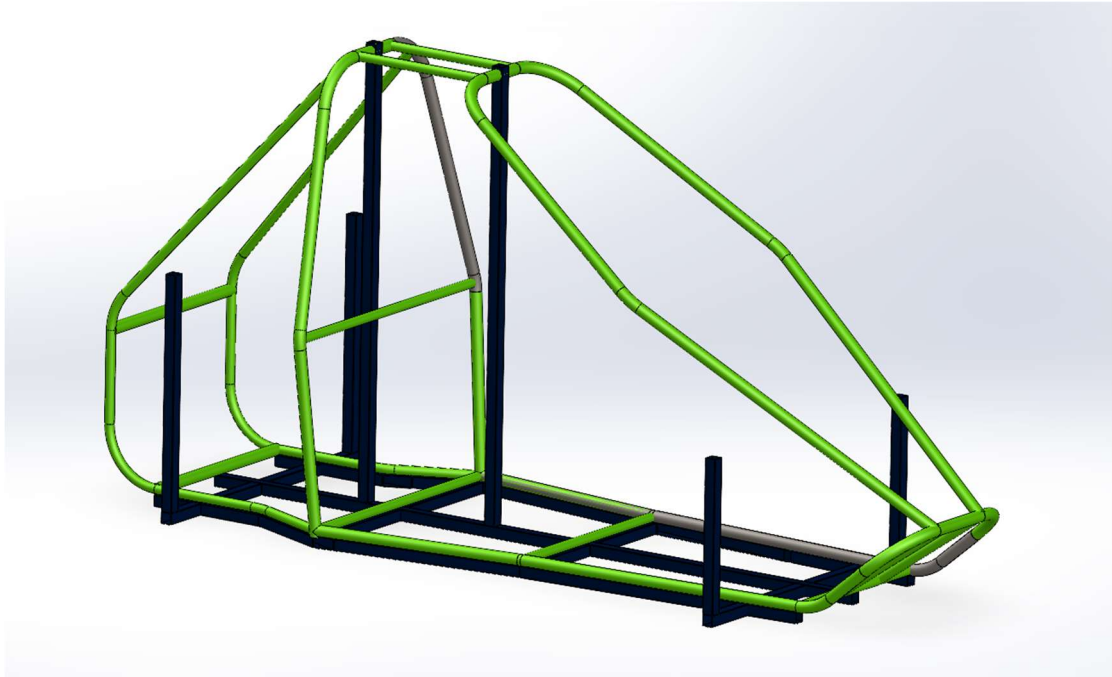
Diseño del bastidor sobre el Jig de soldadura
